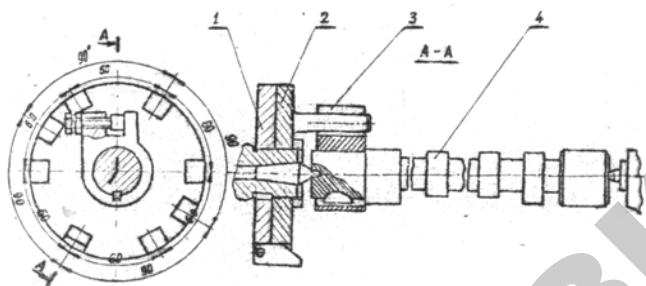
Схема установки распределительного вала для шлифования кулачков с применением делительного приспособления:
